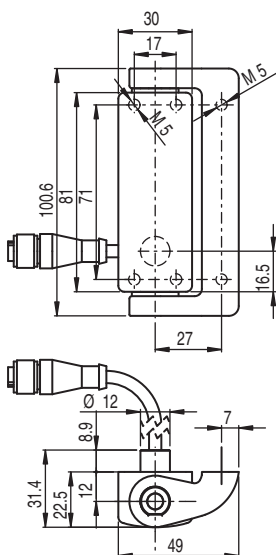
Dimensioni dell'S400-Mx-CB02M12-W in mm
